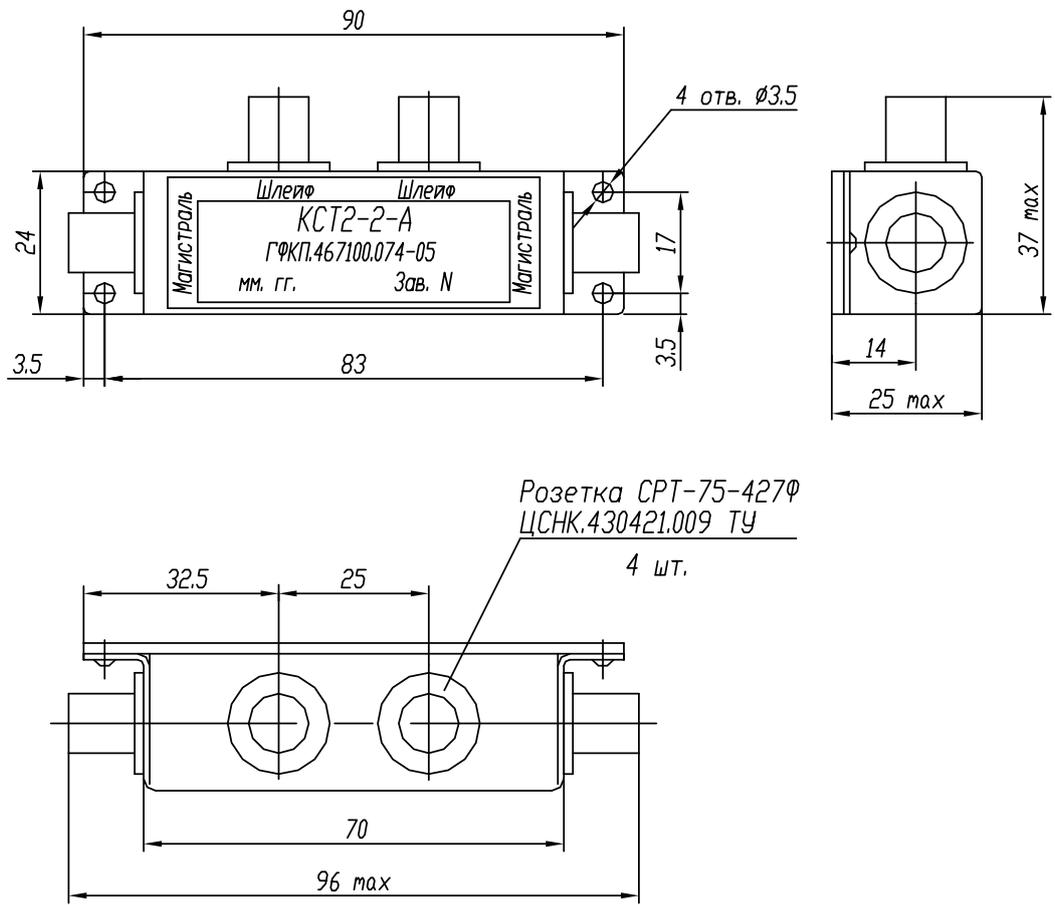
Габаритный чертеж коробки соединительной КСТ2-2
